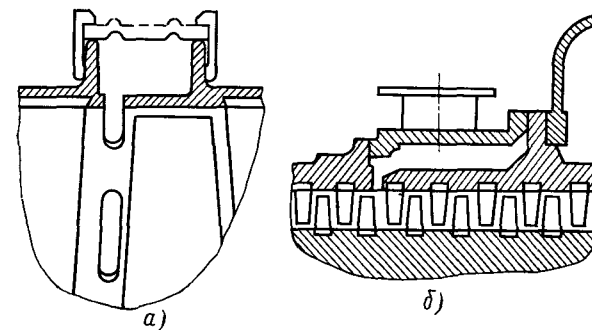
Камеры для отбора воздуха в компрессорах ГТУ:
